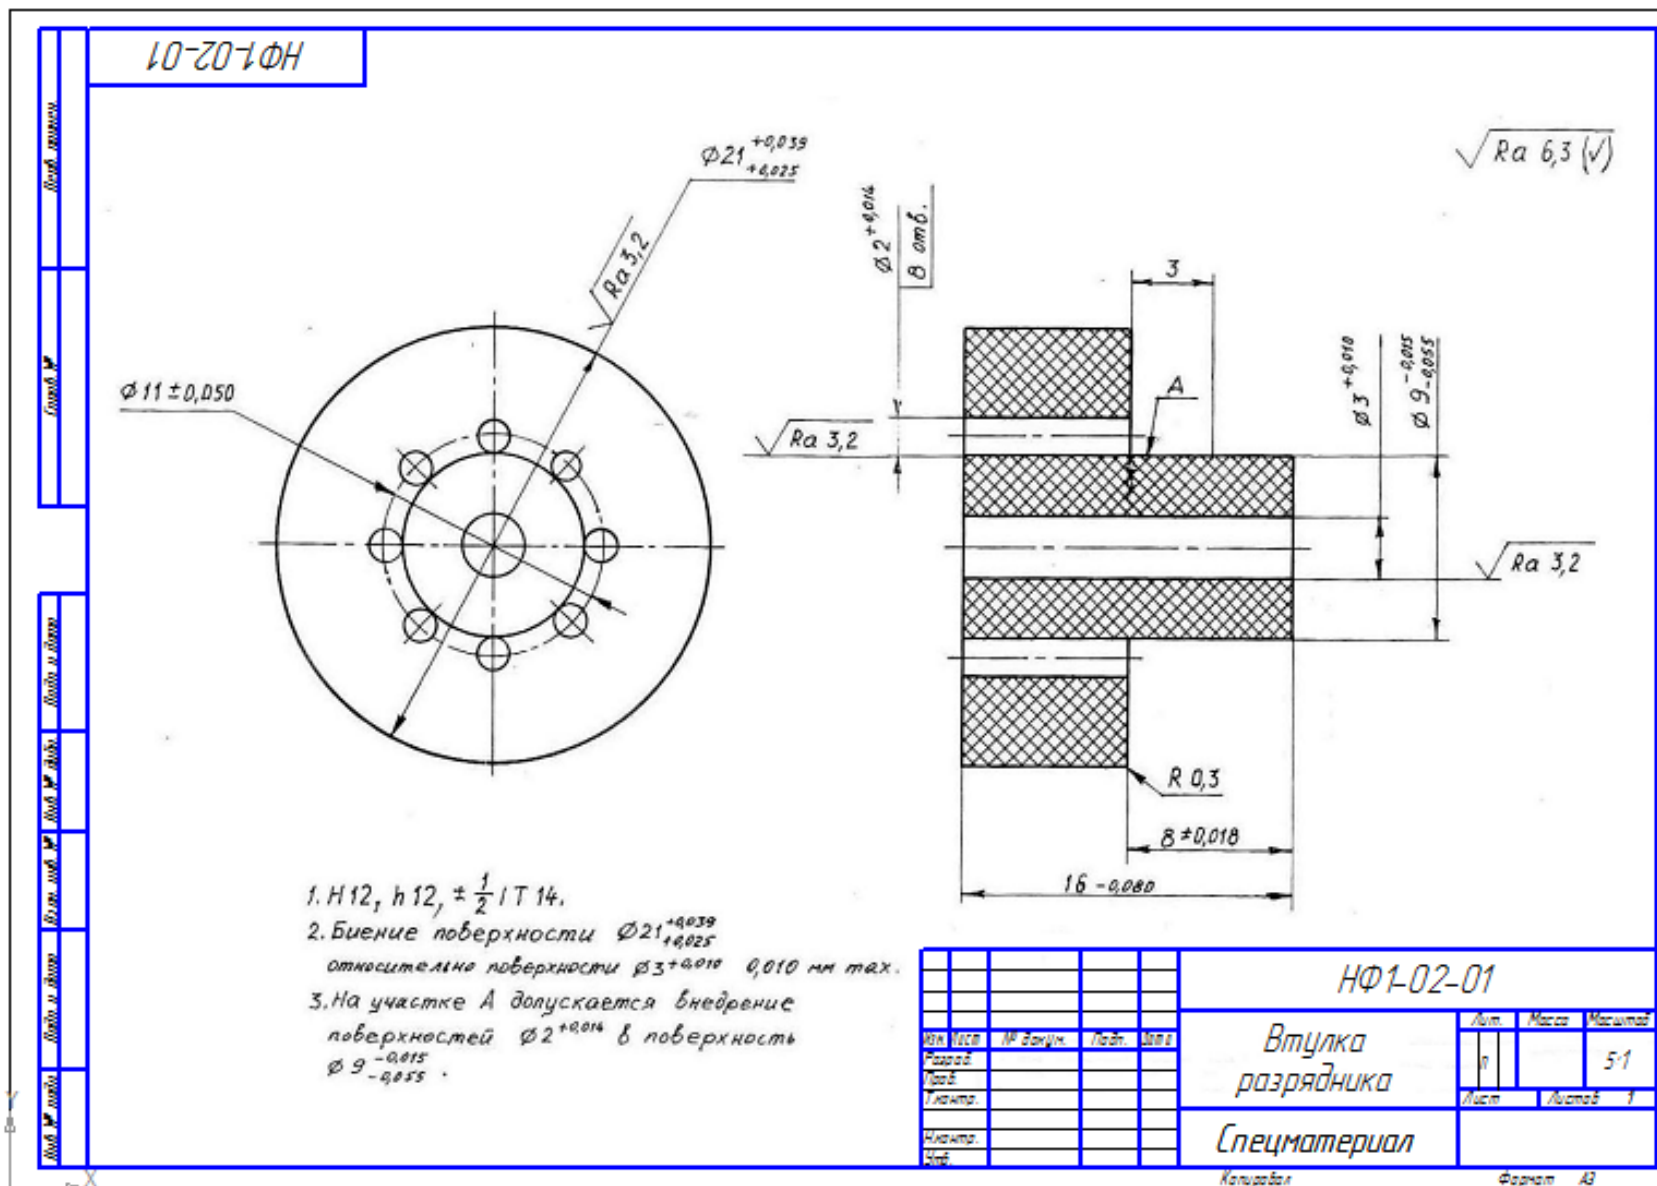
Пример выполнения рабочего чертежа детали «Втулка разрядника»
